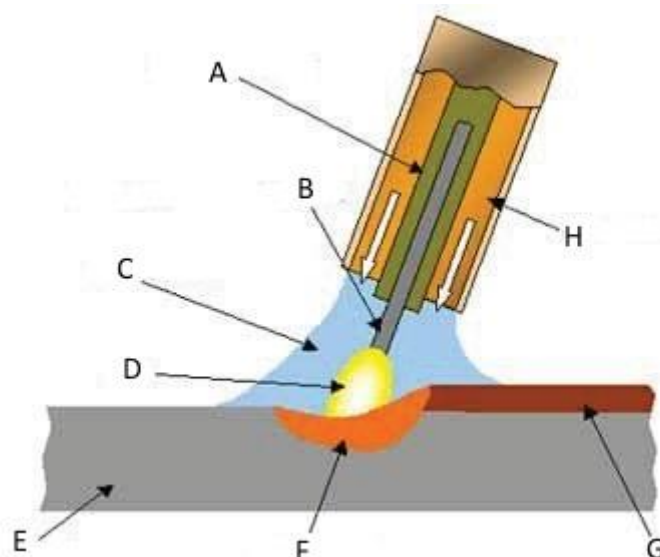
El proceso de soldadura MAG. A. Tubo de contacto, B. Electrodo consumible, C. Cortina de gas, D. Arco, E. Pieza de trabajo, F. Baño de soldadura, G. Metal de soldadura, H. Boquilla de gas. Fuente: TWI
